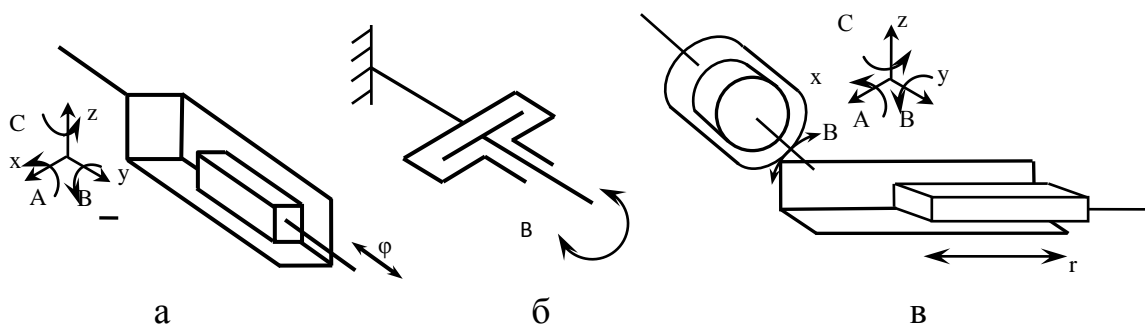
Кінематичні схеми приводів: а - однокоординатний привід поступального руху; б – привід обертального руху; в – двохкоординатний привід комбінованого обертального і поступального руху
